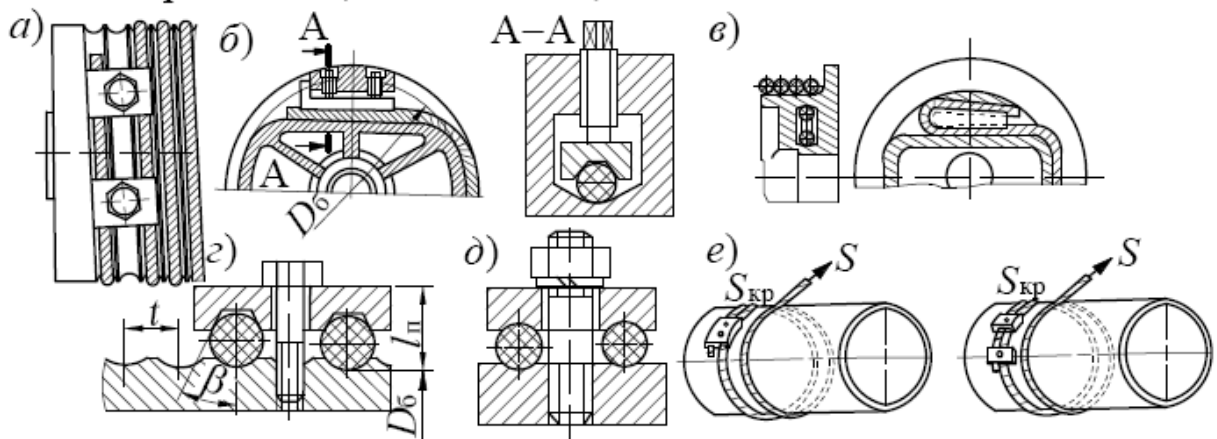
Схемы крепления каната на барабане: *а* – накладкой; *б* – прижимной планкой; *в* – клиновым зажимом; *z, д* – одноболтовой накладкой с трапецидальной или полукруглой канавкой; *е* – схема крепления каната к барабану накладками
